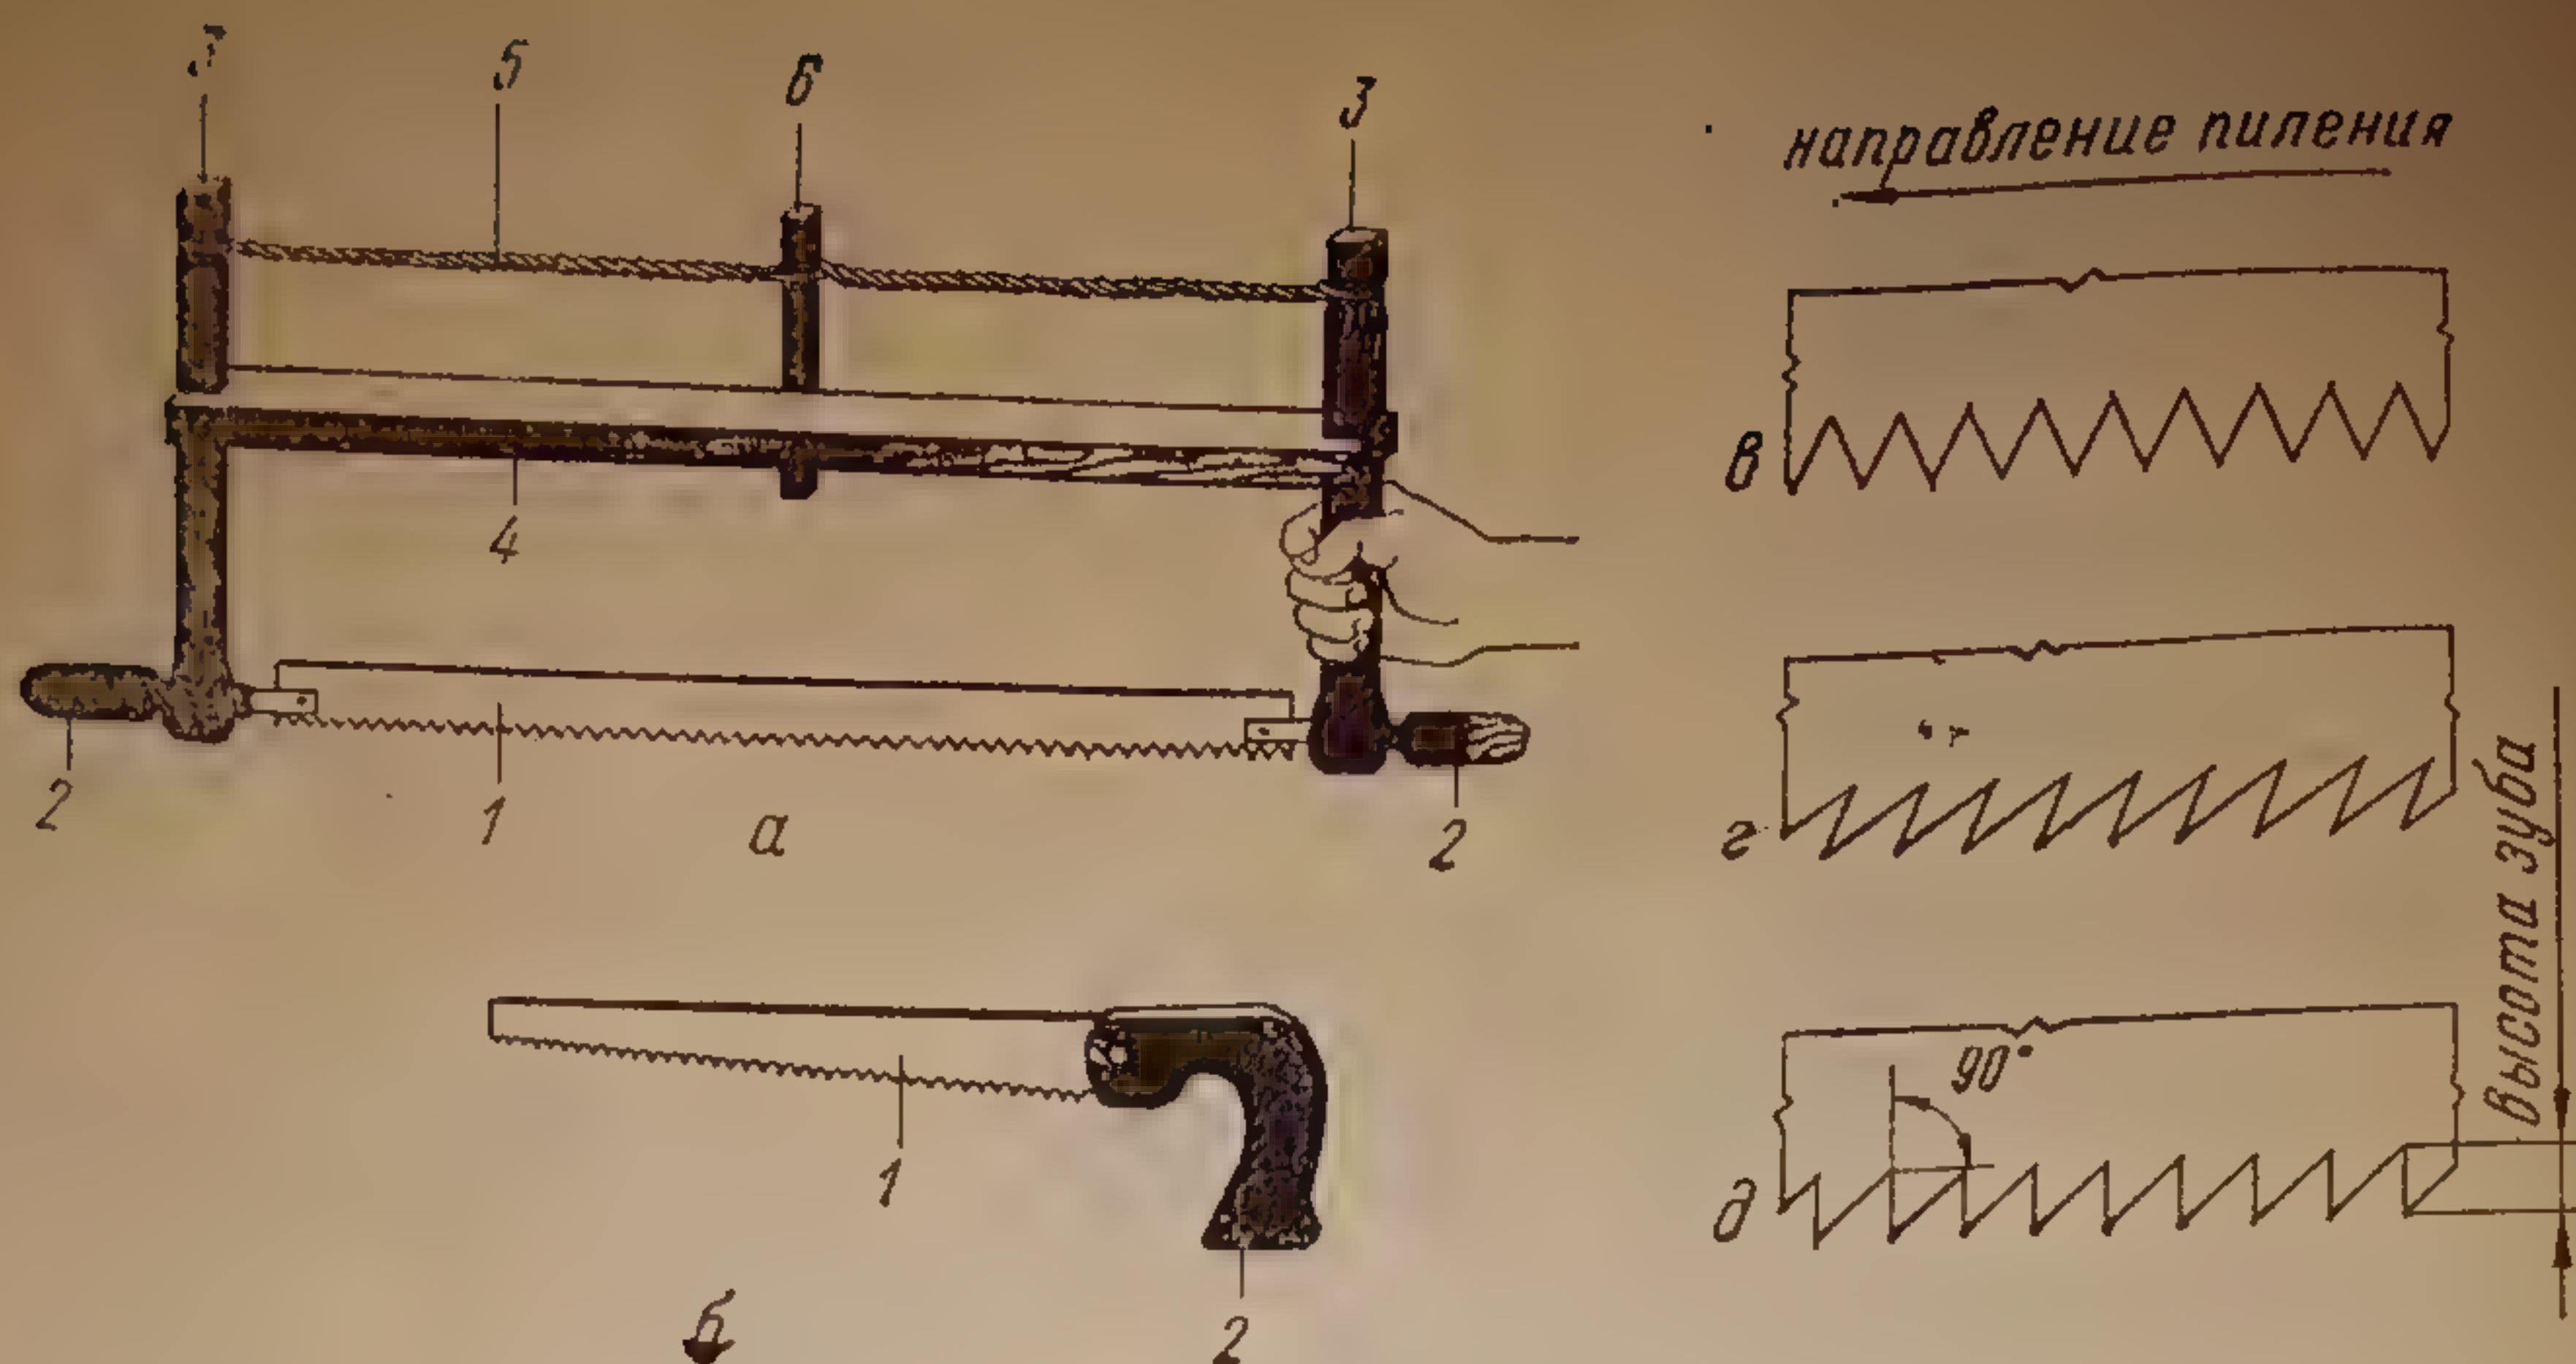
Инструменты для пиления: а — лучковая пила; б — ножовка; в, г, д — зубья пилы; 1 — пильное полотно; 2 — ручка; 3 — стойка; 4 — распорка; 5 — тетива; 6 — закрутка
